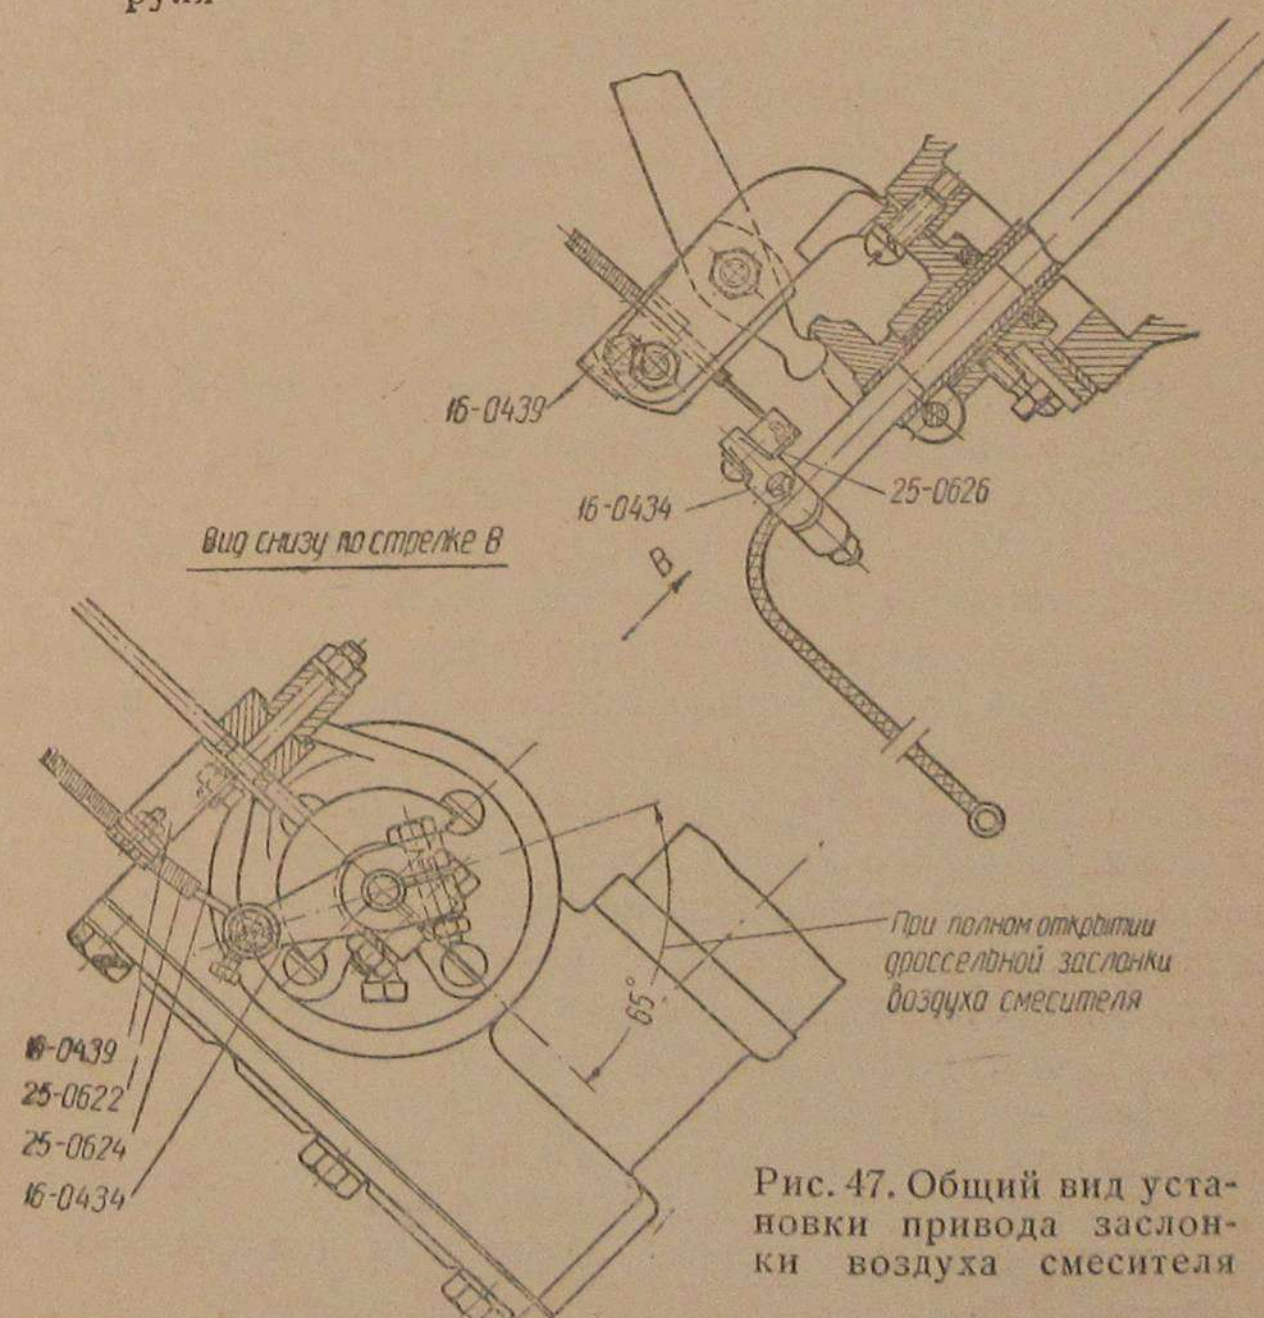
Общий вид установки привода заслонки воздуха смесителя
